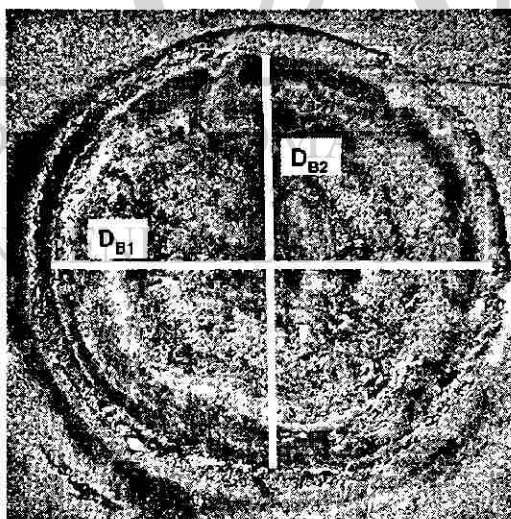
Patrón de medición del diámetro de un botón de soldadura.
